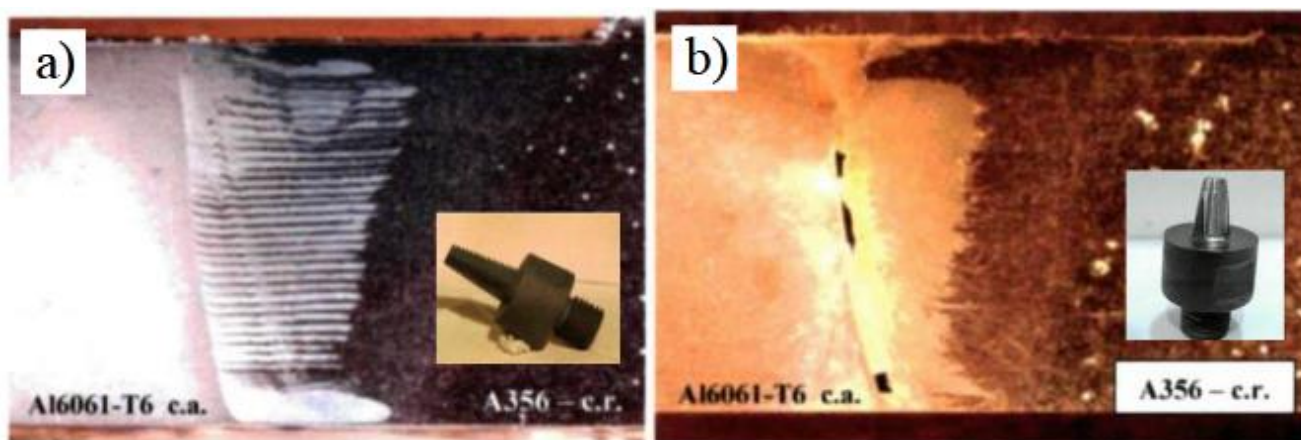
Soudure dissimilaire d'une plaque de 12,7 mm avec a) un outil fileté b) un outil lisse. [12]
